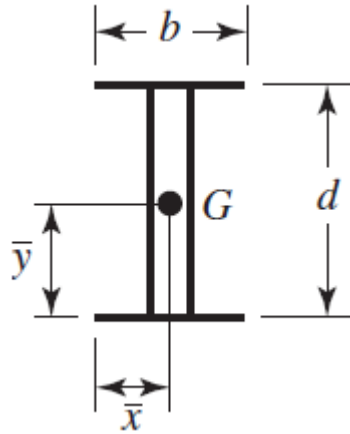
Patrón de soldadura del soporte para la viga carrilera
